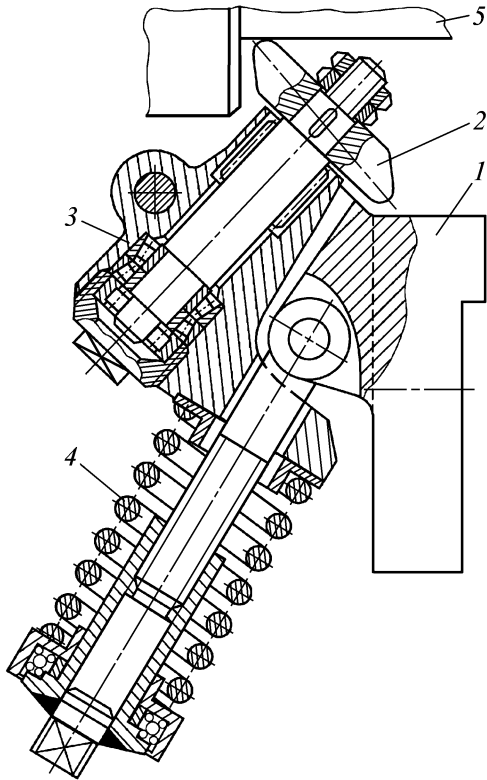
Однороликовое приспособление для обкатывания переходных поверхностей:
